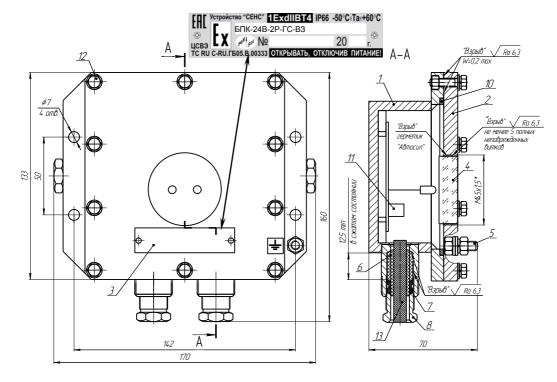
БПК в пластиковом корпусе. Внешний вид, габаритные и установочные размеры
